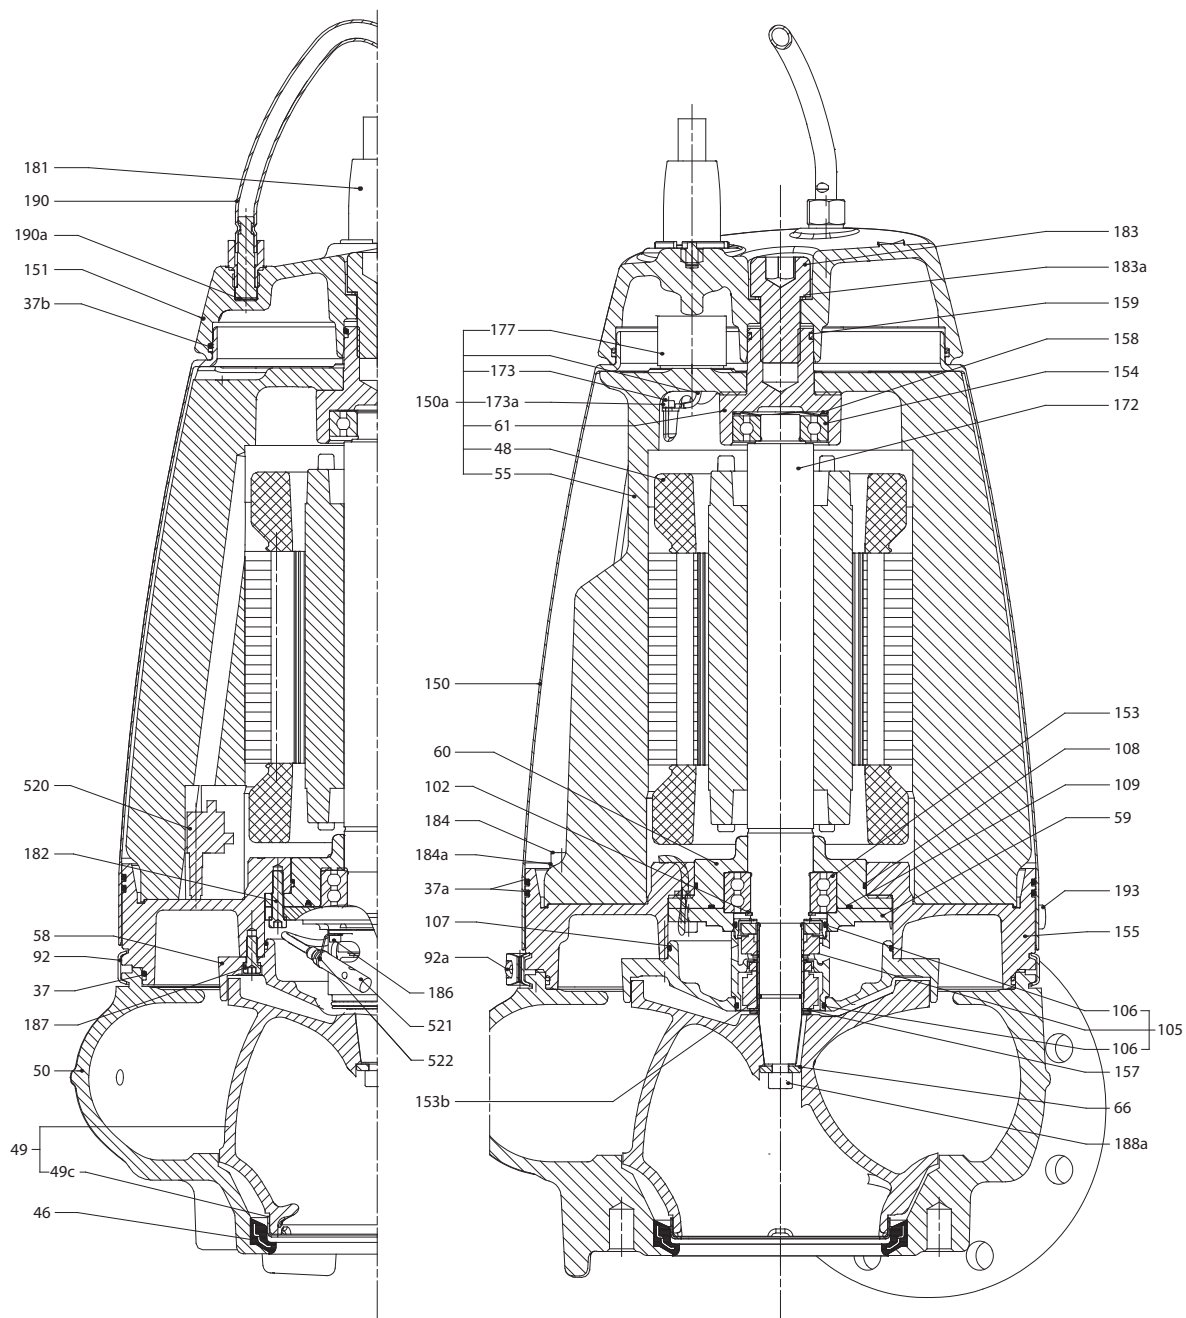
Чертеж в разрезе, насос SE1 с одноканальным рабочим колесом S-tube (исполнение с датчиками)
